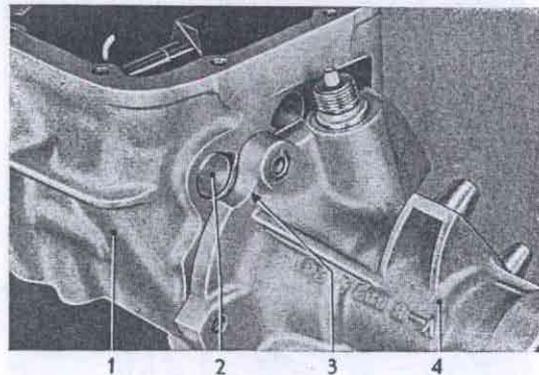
Getriebegehäuseverlängerung um Hauptwelle gedreht, bis Achse für Rücklaufrad freiliegt
